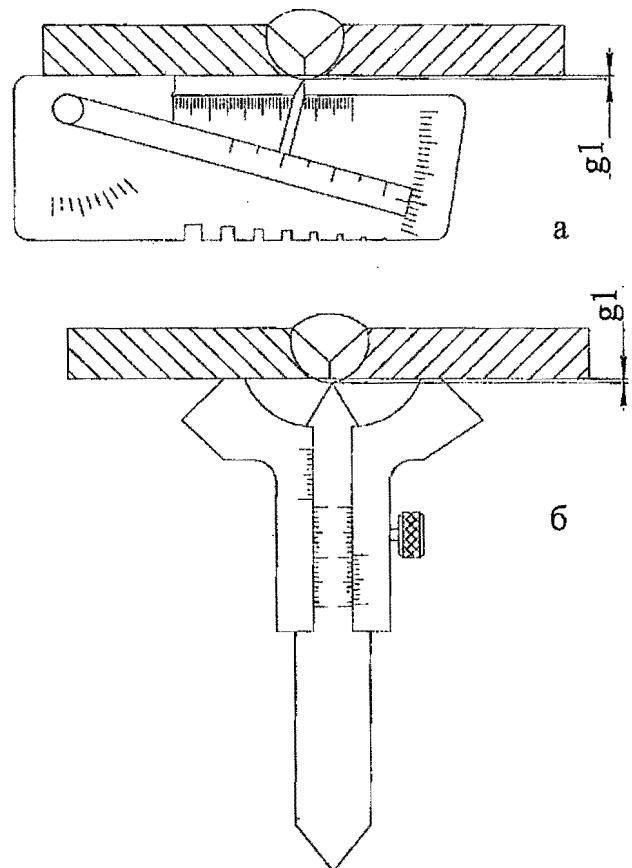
13. Измерение выпуклости (вогнутости) корня шва (g_1) стыкового сварного соединения:
